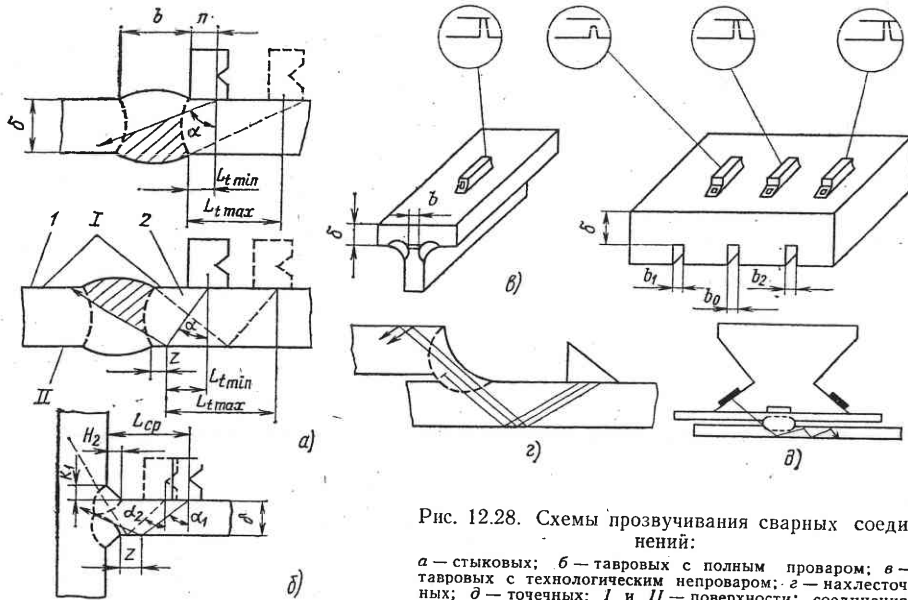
Схемы прозвучивания сварных соединений: а — стыковых; б — тавровых с полным проваром; в — тавровых с технологическим непроваром; г — нахлесточных; д — точечных; 1 и II — поверхности соединения; 1, 2 — стороны соединения
